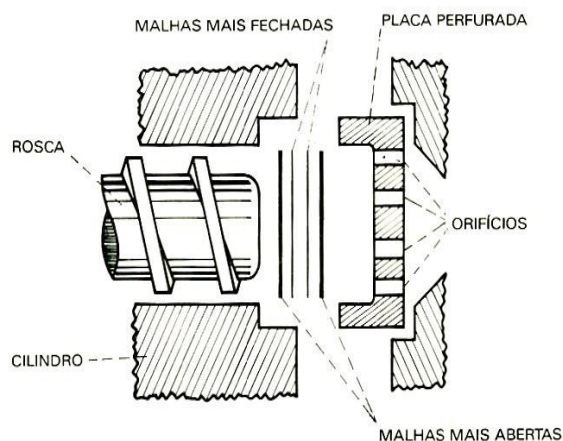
Filtro de telas das extrusoras de reciclagem.
